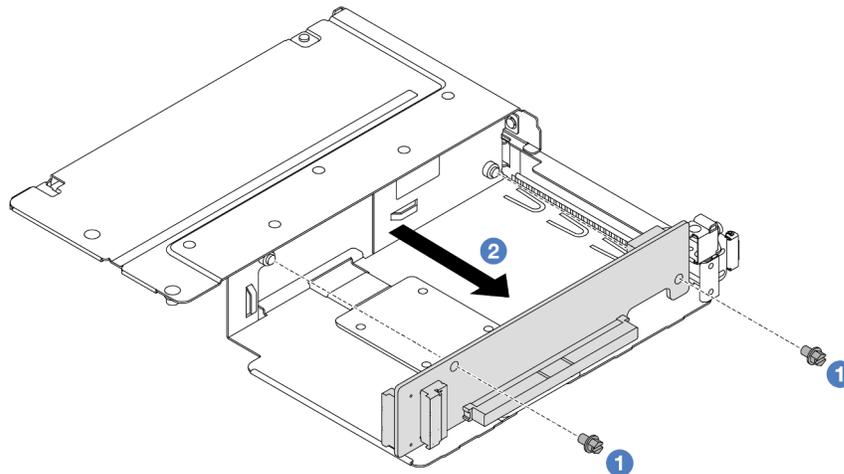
Entfernen der Adapterkarte aus dem Adapterrahmen mit Standardhöhe
